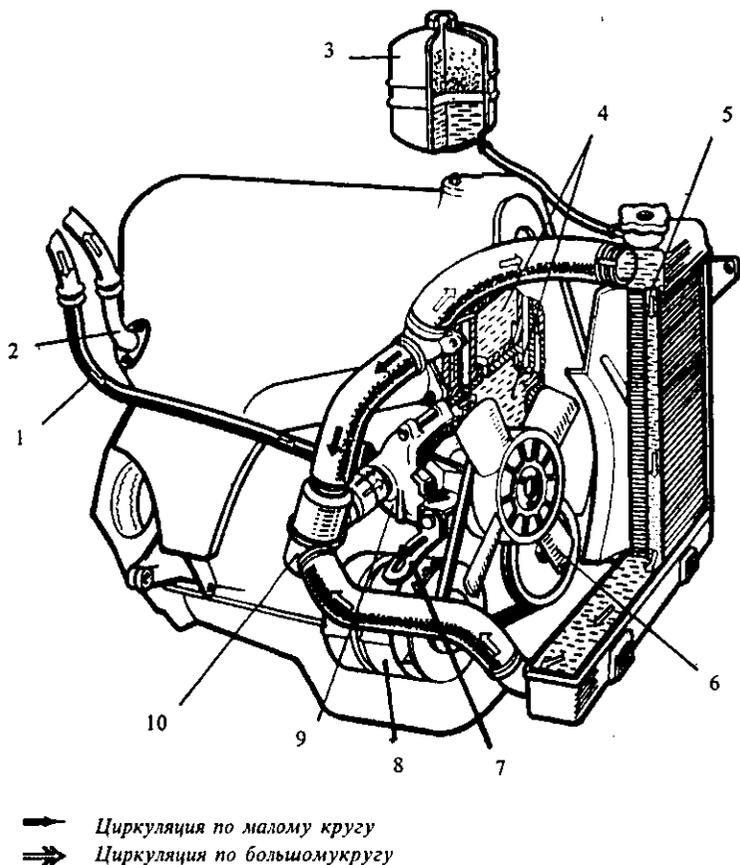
Схема жидкостного охлаждения двигателя ВАЗ-2105:
